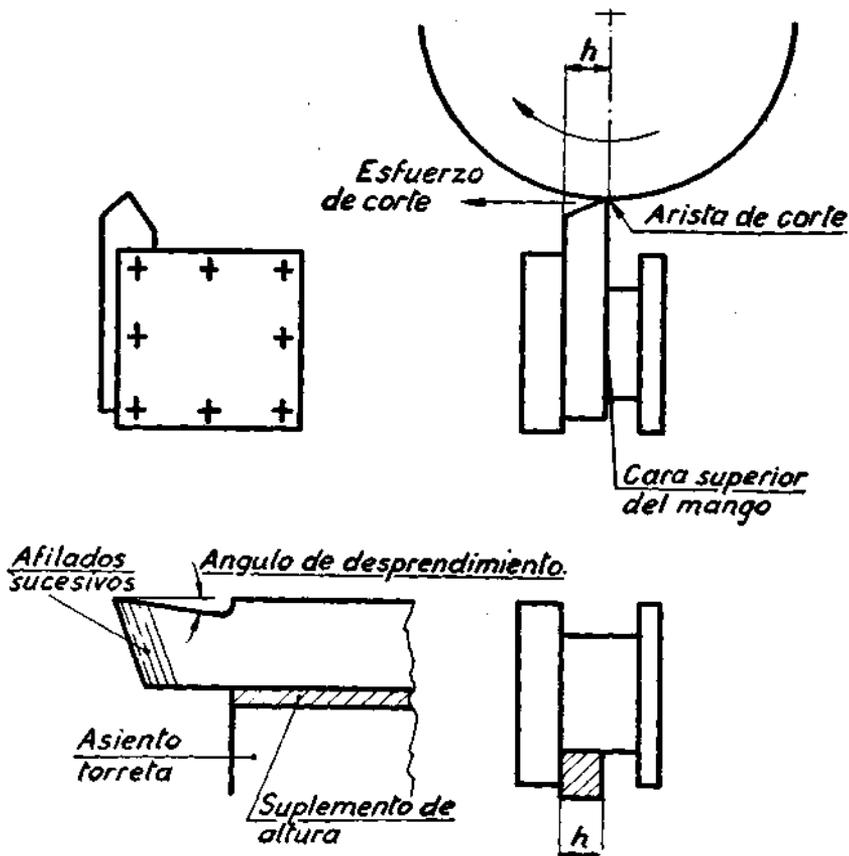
Dimensiones del mango de la herramienta. — h = altura del mando.
